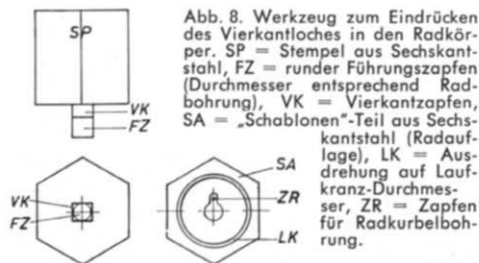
Werkzeug zum Eindrücken des Vierkantloches in den Radkörper. SP = Stempel aus Sechskantstahl, FZ = runder Führungzapfen (Durchmesser entsprechend Radbohrung), VK = Vierkantzapfen, SA = „Schablonen“-Teil aus Sechskantstahl (Radauf-lage), LK = Ausdrehung auf Laufkranz-Durchmesser, ZR = Zapfen für Radkurbelbohrung.
